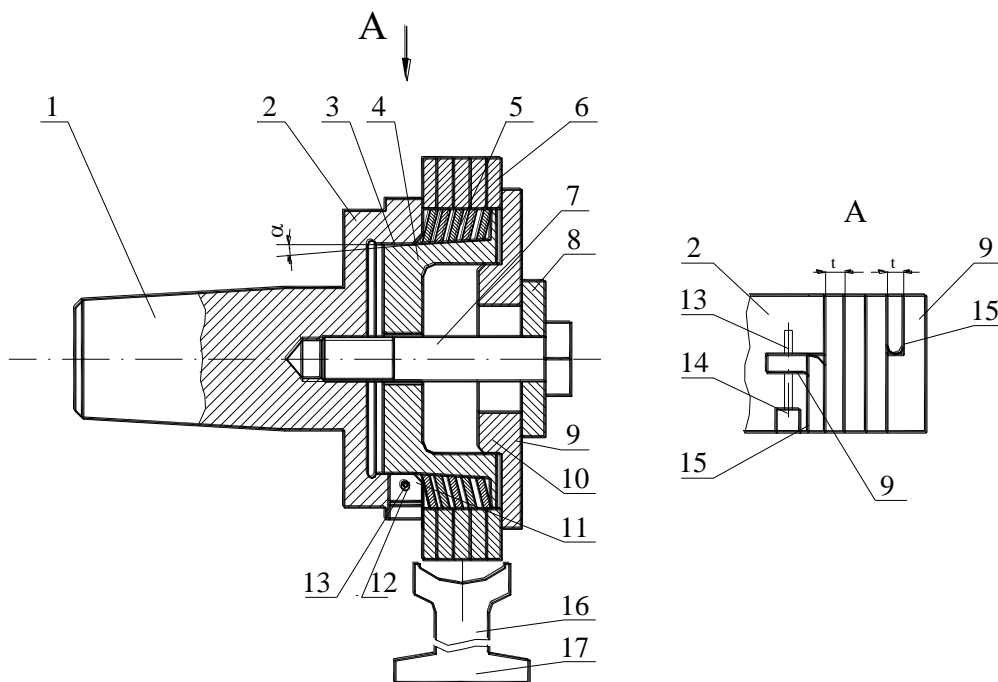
Принципова схема оправы для профілювання гвинтових заготовок
